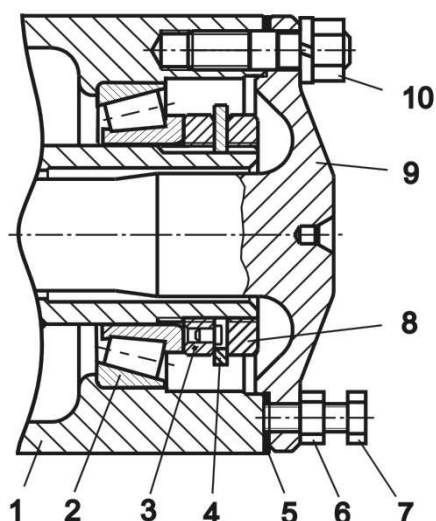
Крепление ступицы заднего колеса ("КААЗ")
